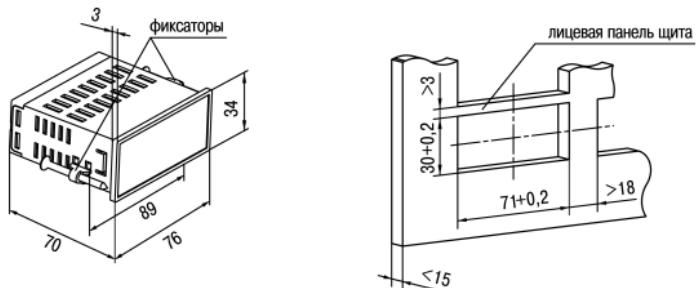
Габаритные размеры корпуса ЩЗ
